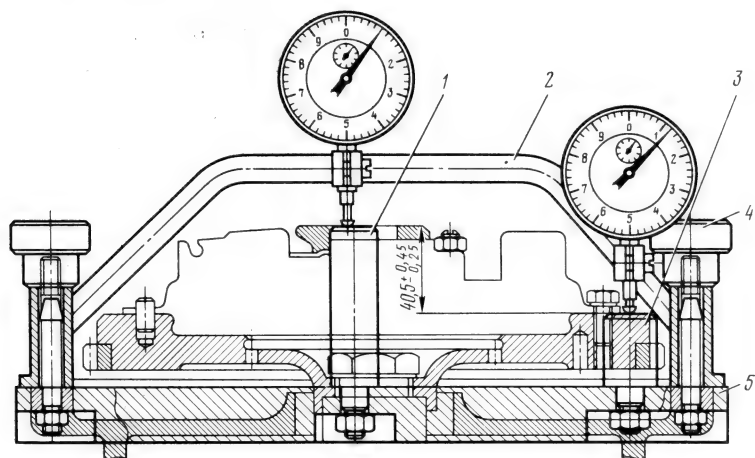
Приспособление для проверки биения торца маховика и для регулировки положения пяты рычагов сцепления:
